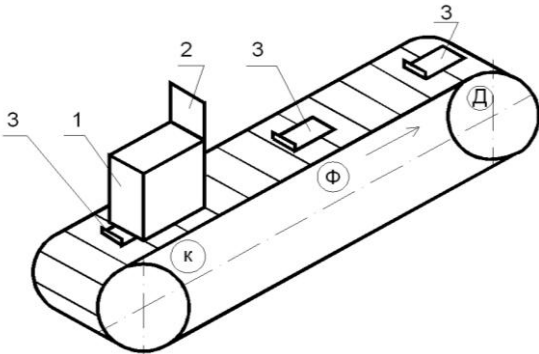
Механічний пристрій для автоматичного формування картонних пачок: 1 – магазин; 2 – засув; 3 – лотки
